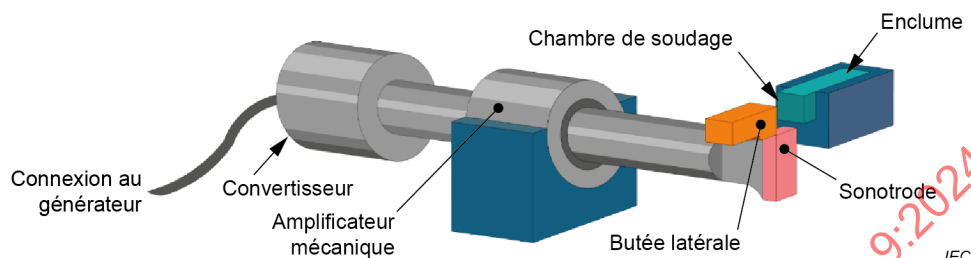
Machine de soudage par ultrasons conçue pour réaliser des épissures entre au moins deux fils
